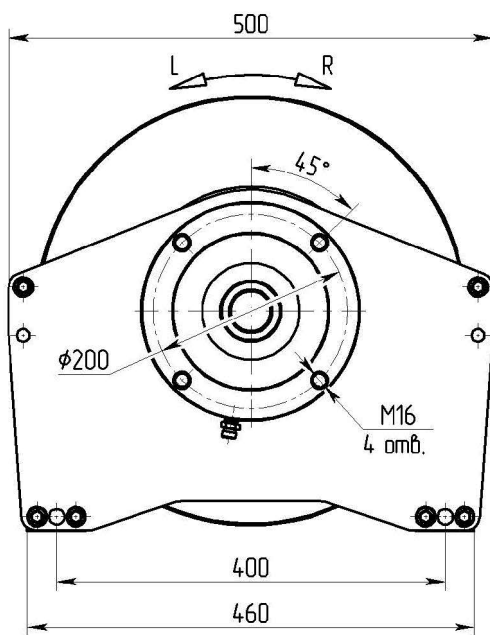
Общий вид лебедки, габаритные и присоединительные размеры
